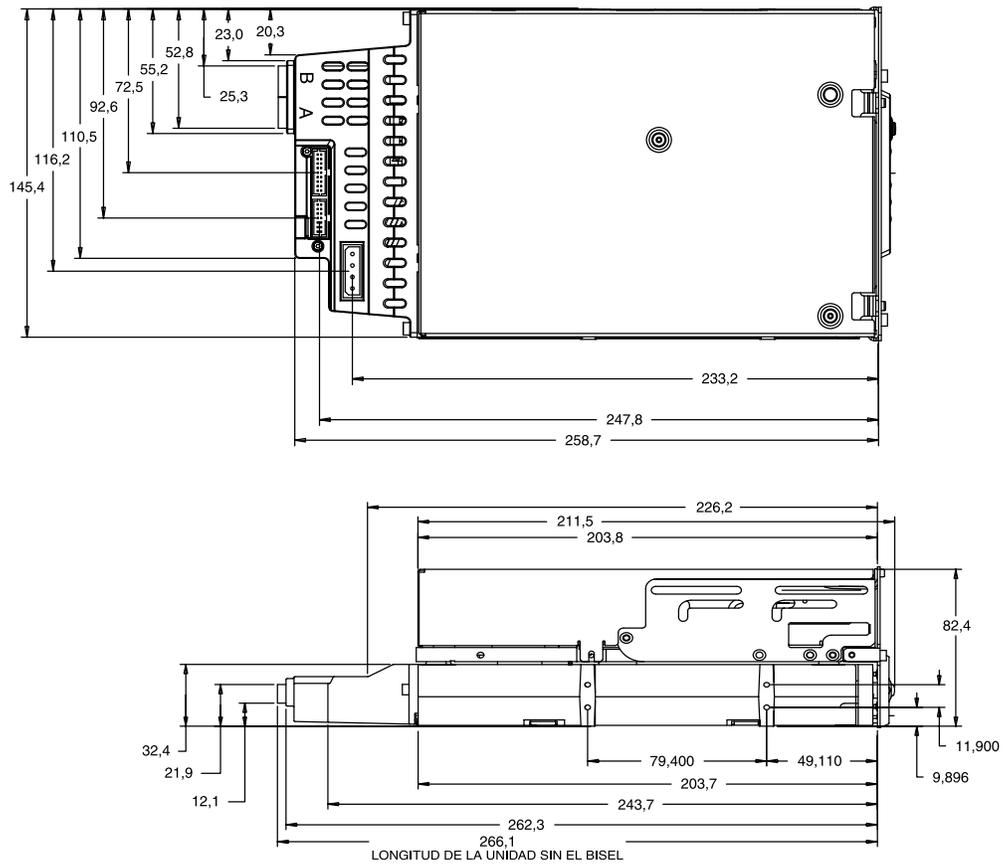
Dimensiones de la unidad interna LTO-1 Fibre Channel
